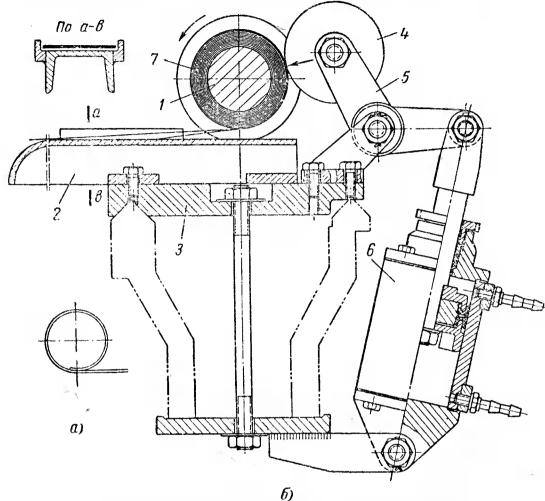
Приспособление для намотки магнитопровода регулятора напряжения АРН-250.
